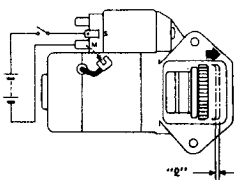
Выступ ведущей шестерни стартера S114-317A (См. Раздел 12)
